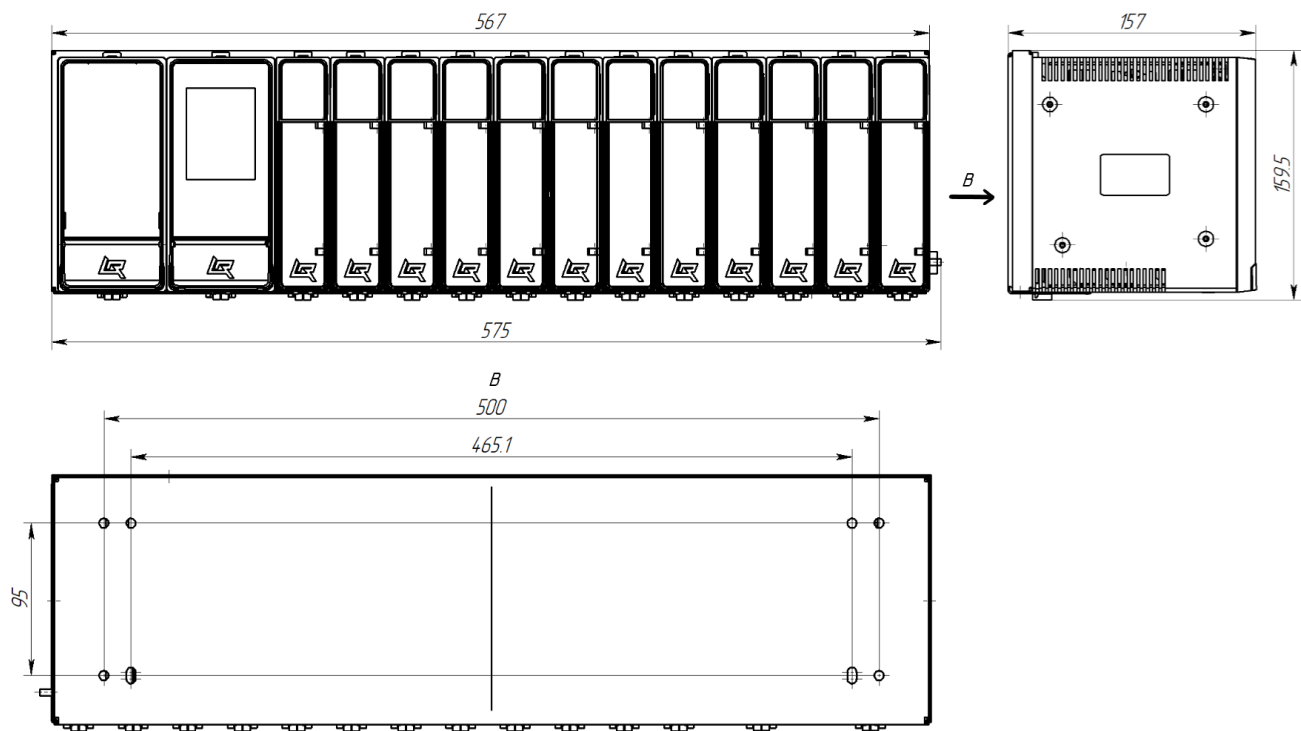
Габаритные и присоединительные размеры сборки контроллера на шасси SH-16 с модулями в пластмассовом корпусе
